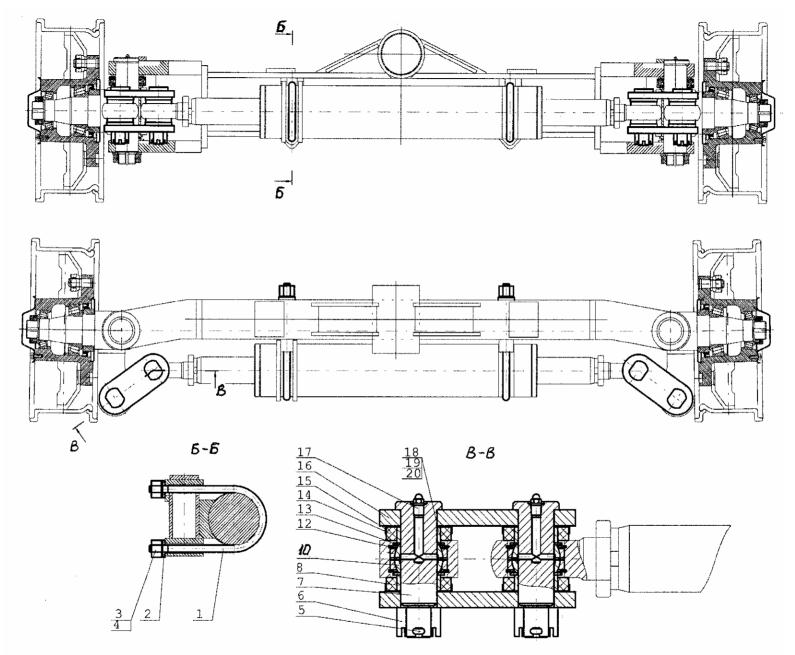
Управление поворотом колес Fig. 49 Steering Gear
